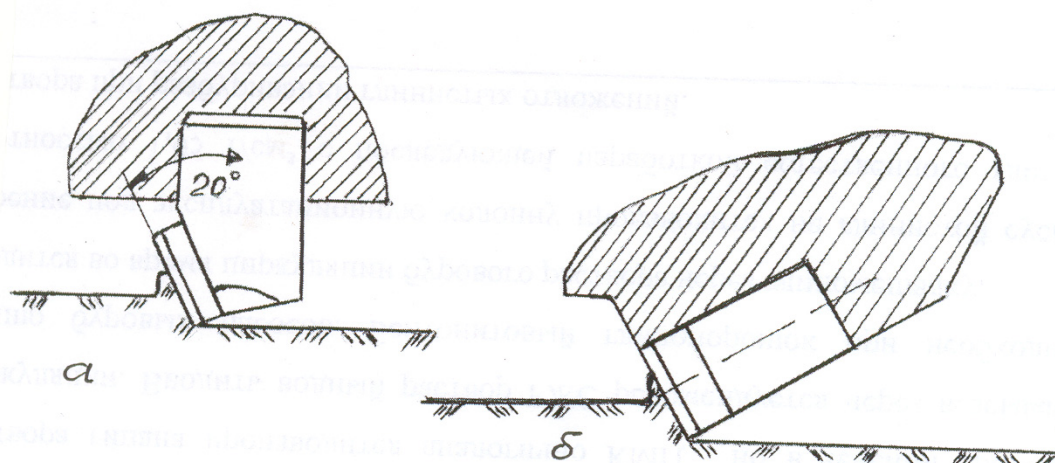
Крепление АТП и АТР к корпусу
